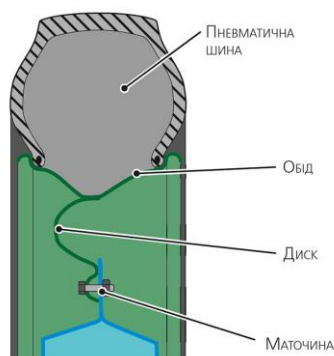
Колісний рушій. Поперечний розріз
